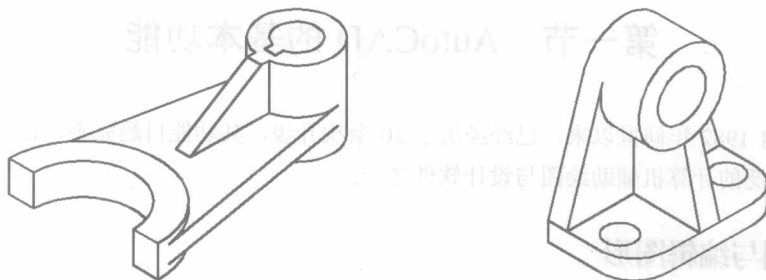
使用 AutoCAD 标注的平面图形和三维图形
